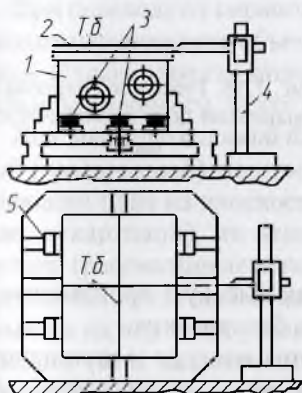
Реальное базирование заготовки в приспособлении-спутнике по разметке
